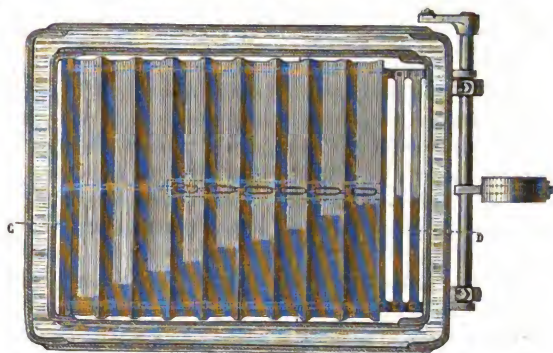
Plan d'un foyer à grille Chobrzynsky.
